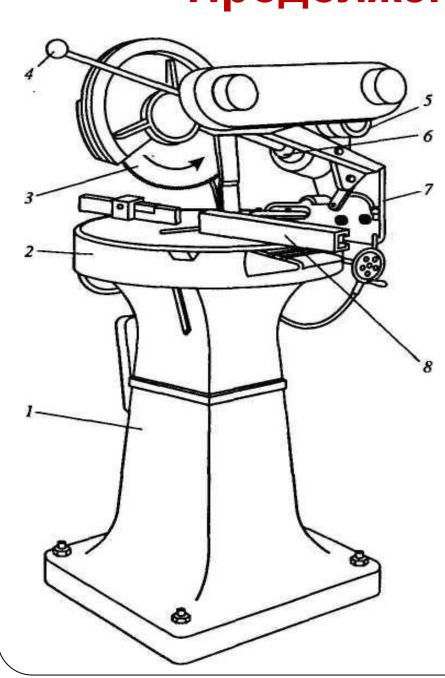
Маятниковая пила: 1 - станина; 2 - стол; 3 - режущий диск; 4 - рукоятка; 5 - шкив; 6 - качающийся хобот; 7 - кронштейн; 8 - опорная планка
